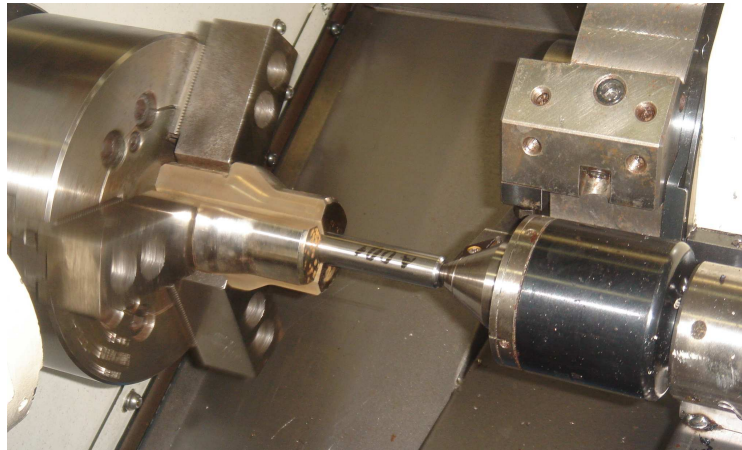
Imagem das castanhas adaptáveis montadas no torno.
